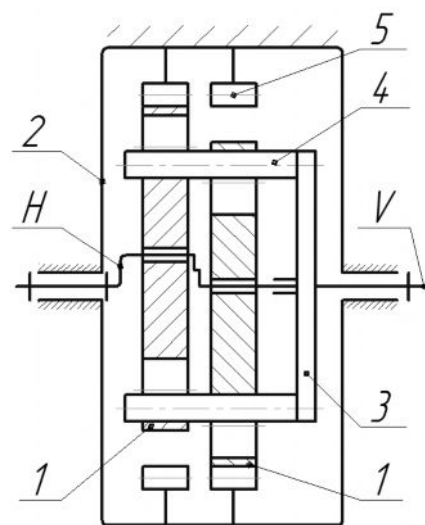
Схема редуктора типа К-Н-V с двумя сателлитами
